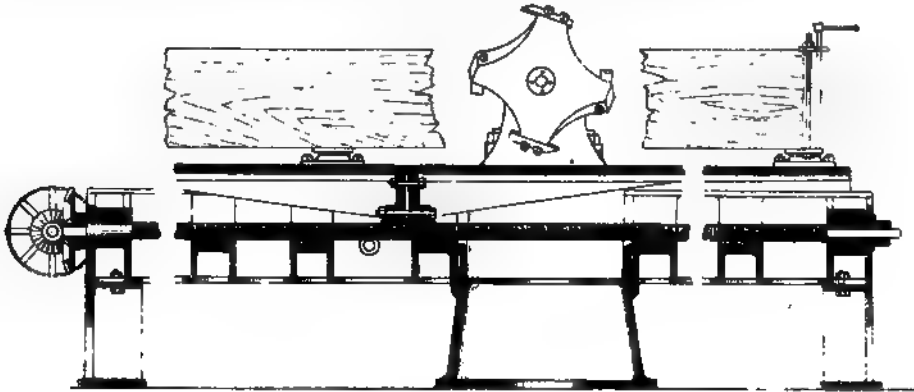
Abricht-hobelmaschine (Längsschnitt).
